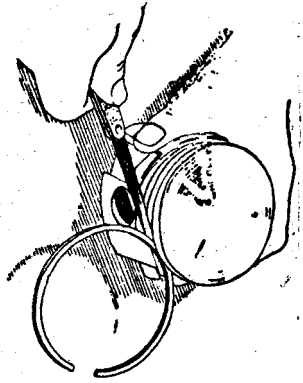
Проверка зазора между поршнем и цилиндром.
